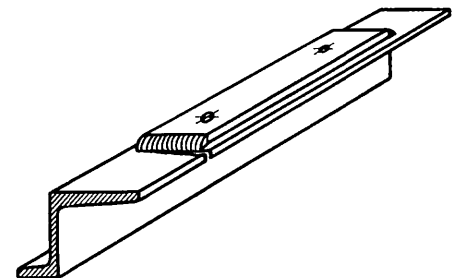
Bruch an einem Längsträger mit aufgeschweißter Motorpaßleiste.
